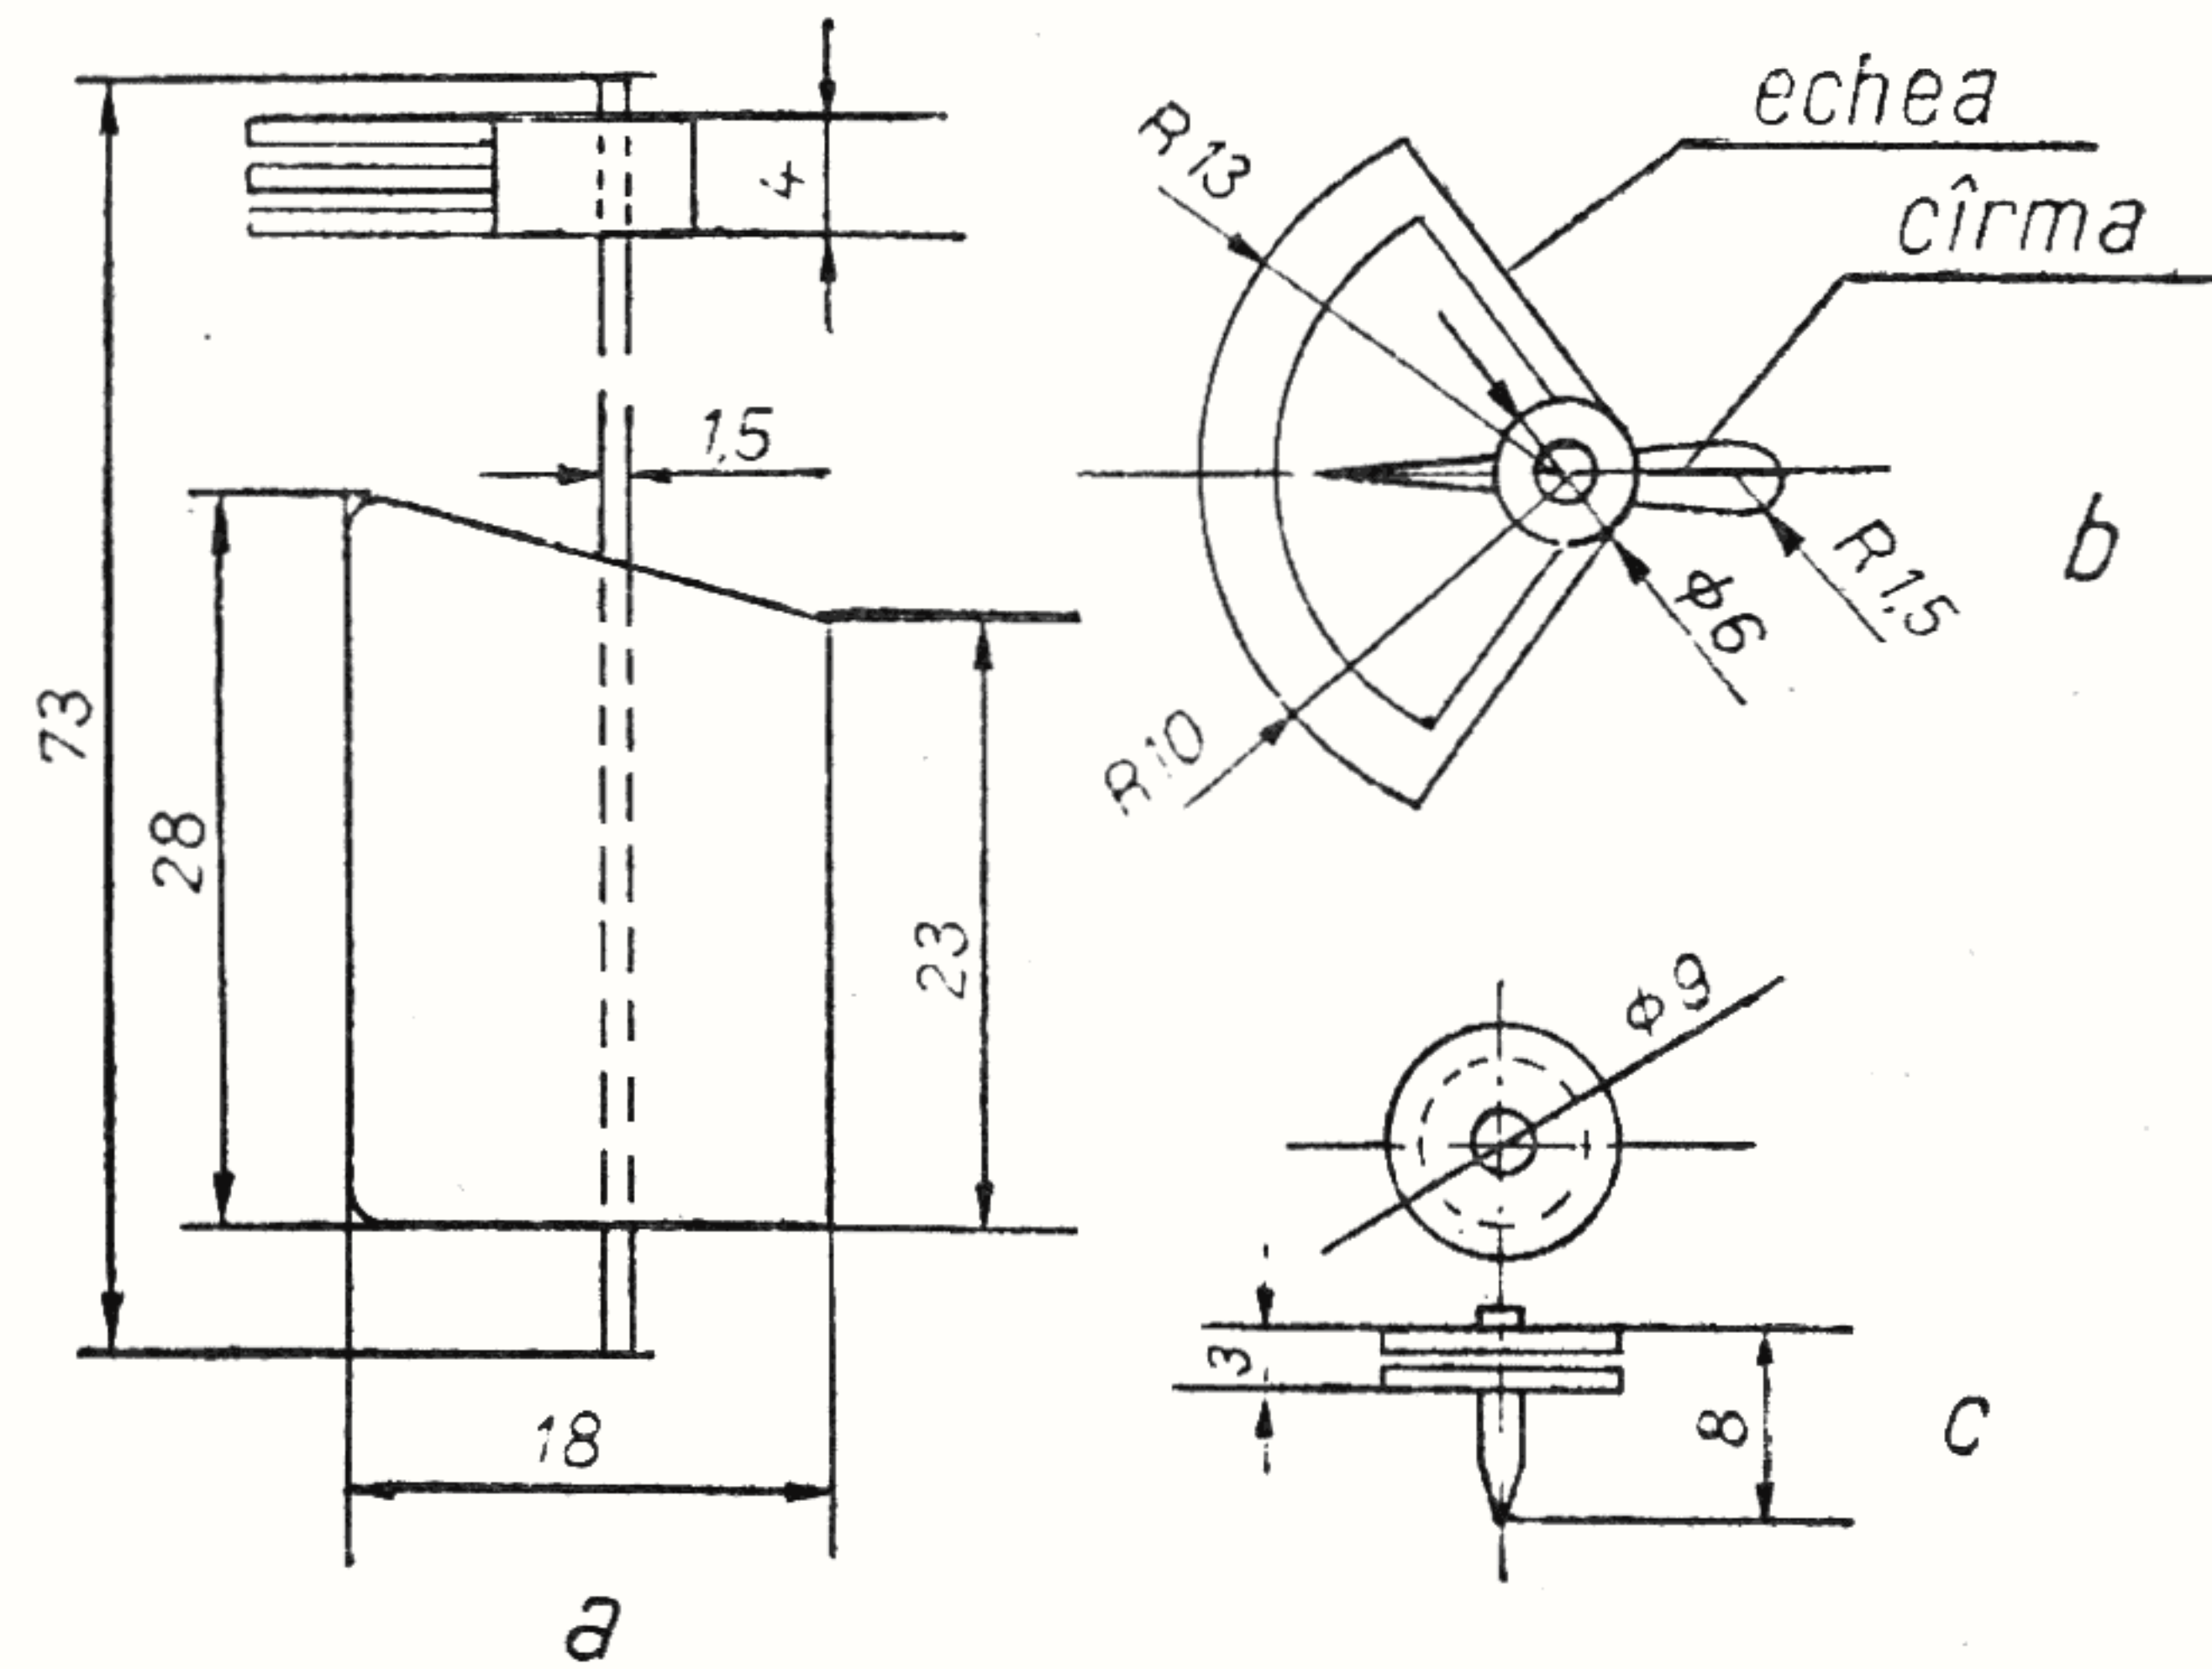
Instalația de guvernare: a) cîrma; b) echea; c) ro-lă pentru dirijat troțele.
